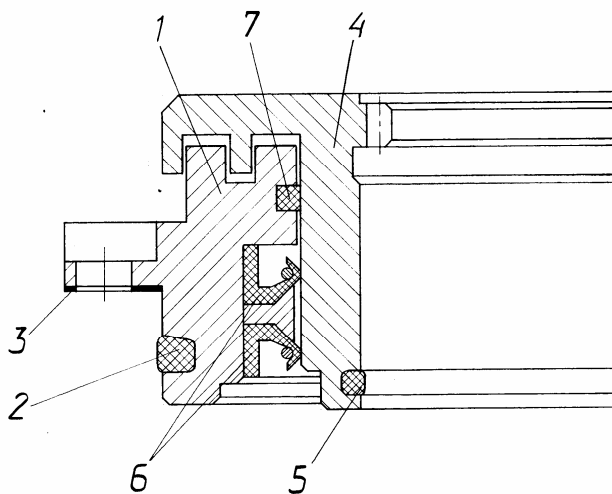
Штатное уплотнение подшипникового узла поворотного редуктора шахтного комбайна
